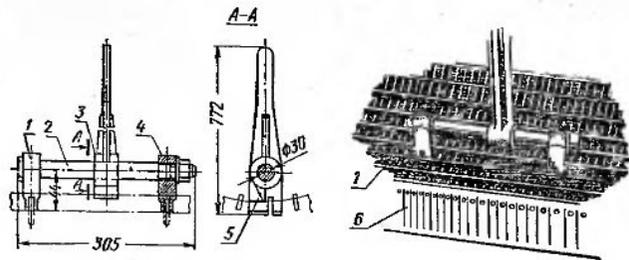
Приспособление для правки поперечного изгиба планок подбаранья:
